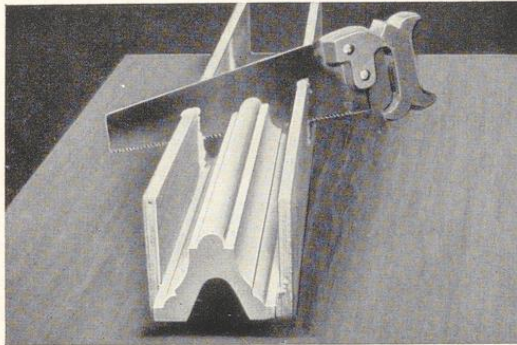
Zuschneiden der Deckenstäbe in der Gehrungslade
